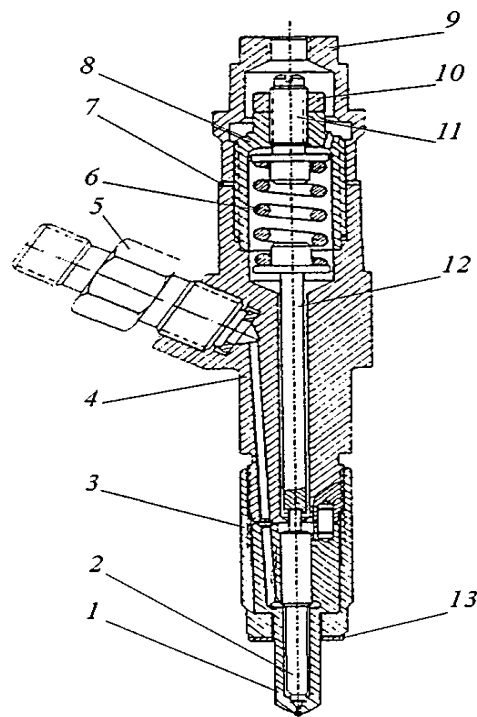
Будова форсунки: 1 - корпус розпилювача; 2 - голка розпилювача ; 3 - гайка розпилювача; 4 - корпус форсунки; 5 - штуцер для підключення паливопроводу ; 6 - пружина; 7, 13 - ущільнення; 8 - пружинна гайка; 9 - ковпачок; 10 - контргайка; 11 - регулювальний гвинт; 12 -
